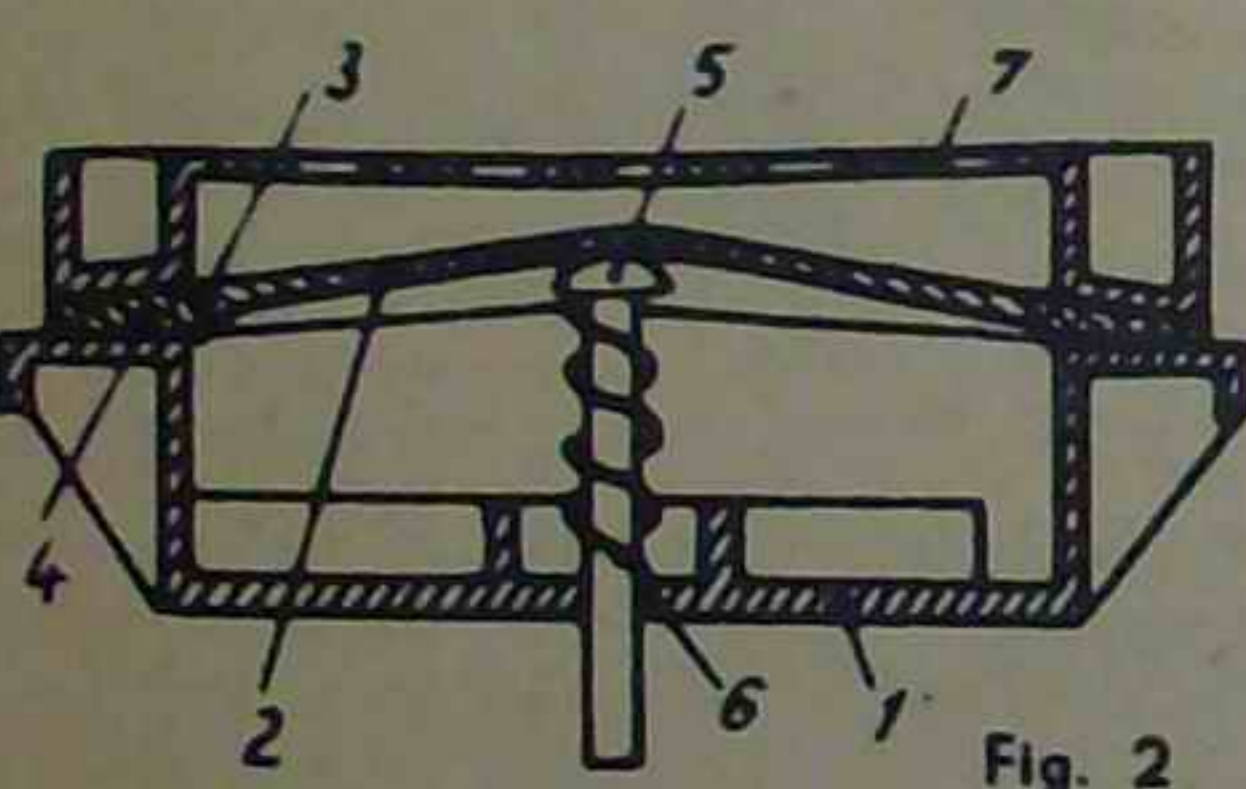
1. corp; 2. electrod; 3. membrană; 4. inel de cauciuc; 5. bol; 6. arc spiral; 7. capac perforat
